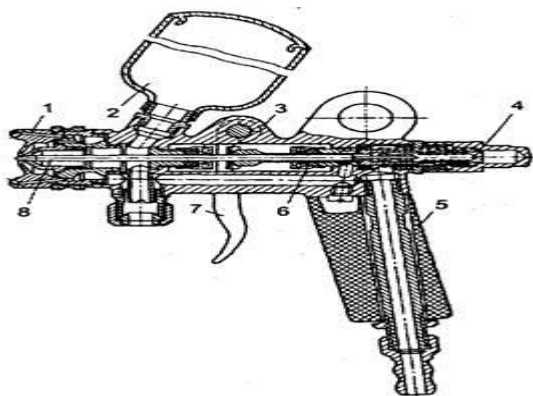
Пневматический пневмораспылитель: 1 — распылительная головка; 2 — бачок для краски; 3 — корпус распылителя; 4 — запорный винт; 5 — ручка; 6 — прокладка; 7 — спусковой крючок; 8 — запорная игла
